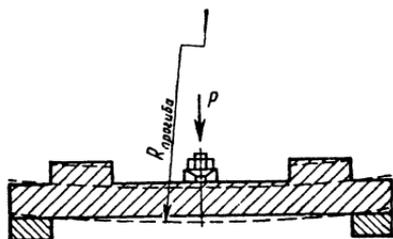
Неправильное крепление заготовки на столе фрезерного станка
